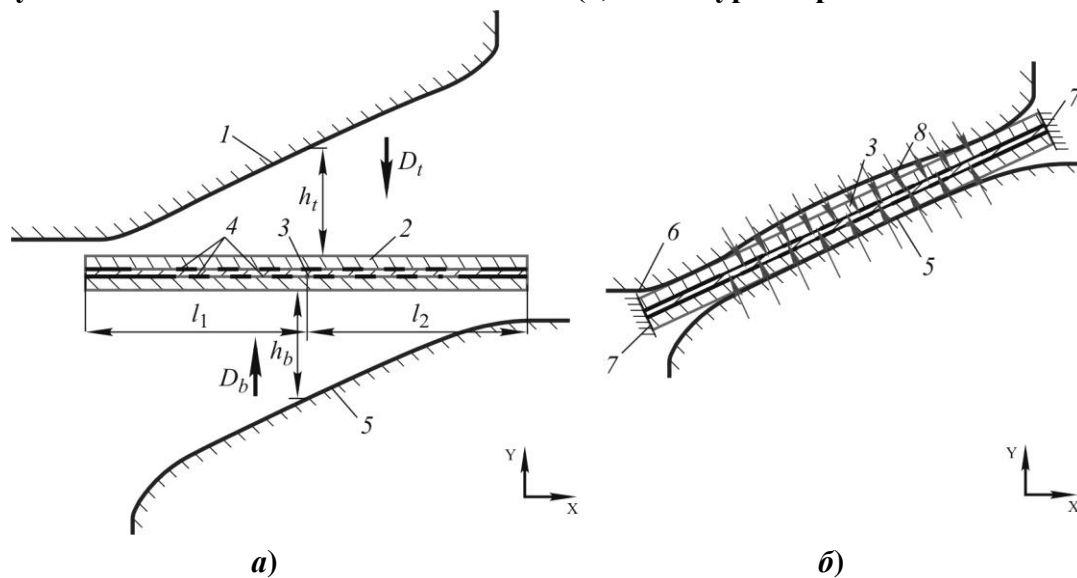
Расчетная схема моделирования операций изотермической штамповки (а) и сверхпластической формовки (б) для полый лопатки вентилятора в 2D постановке: 1 – верхняя матрица; 2 – заготовка; 3 – точка вращения; 4 – зоны сварки; 5 – нижняя матрица; 6 – верхняя матрица для СПФ; 7 – заделка; 8 – внутреннее давление
